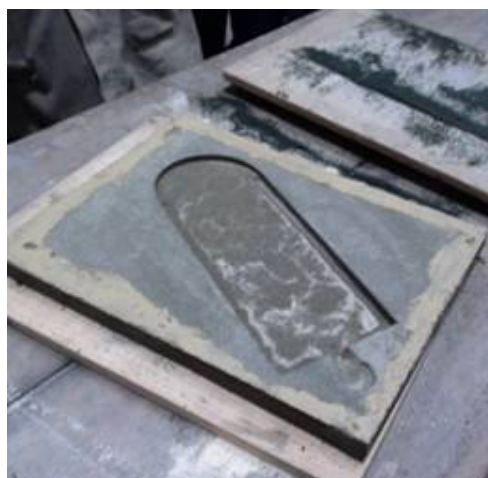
Molde aberto com destaque para o perfil da peça a ser fundida.
